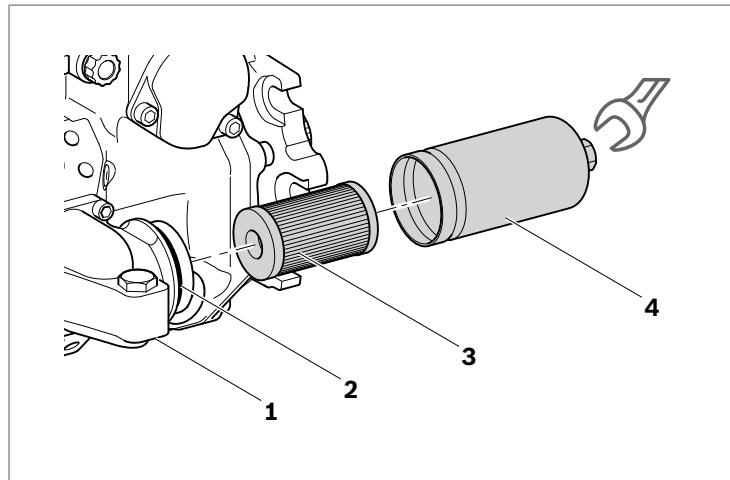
Sostituire l'elemento filtrante del filtro per montaggio a flangia
